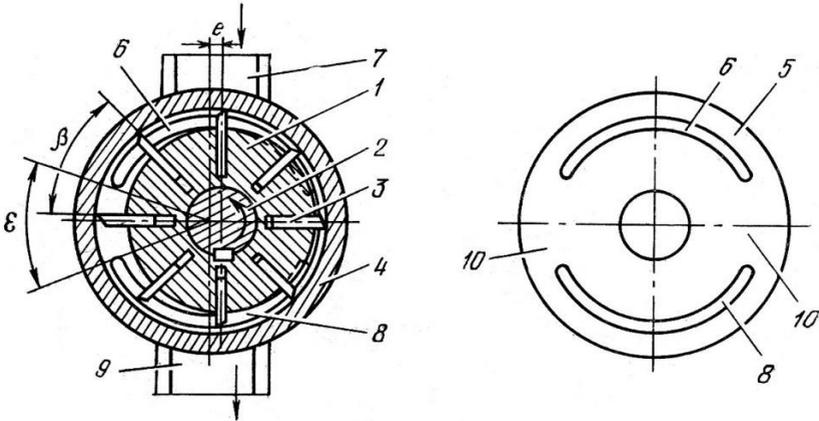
Роторно-пластинчатый насос однократного действия: 1- ротор; 2- вал; 3- пластина; 4- корпус (статор); 5- распределитель; 6- окно гидролинии всасывания; 7; 8- окно гидролинии нагнетания; 9; 10- перемычка
